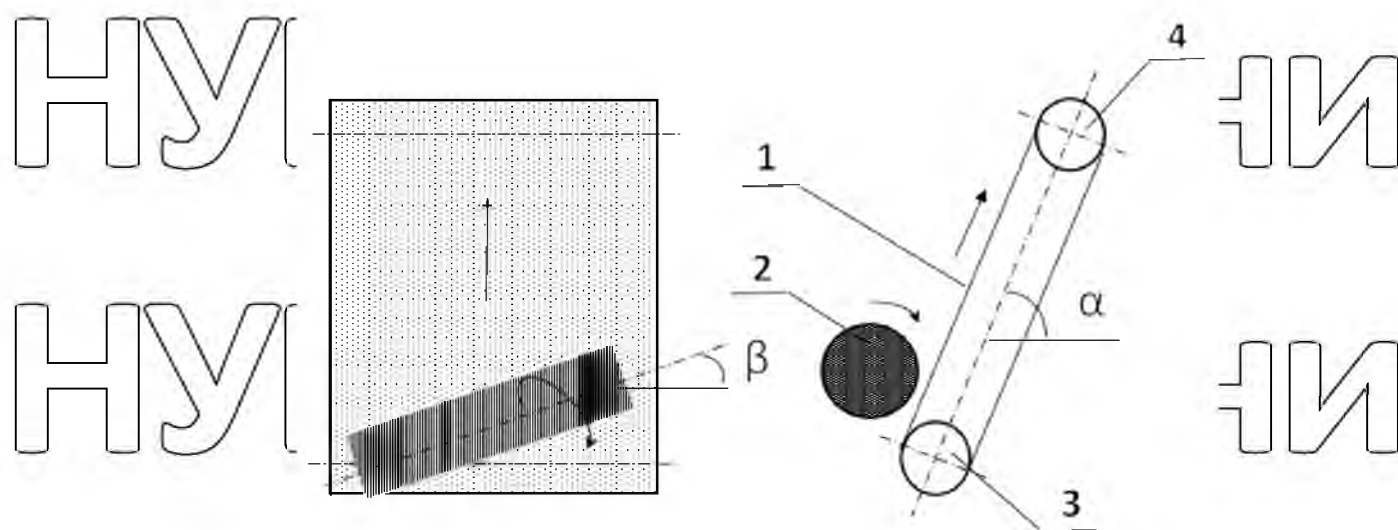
Схема вдосконаленого омишувального робочого органу картоплезбирального комбайна: 1 – похила пальчаста гірка; 2 – валець з еластичною щіткою; 3 – нижній приводний барабан; 4 – верхній напрямний барабан
